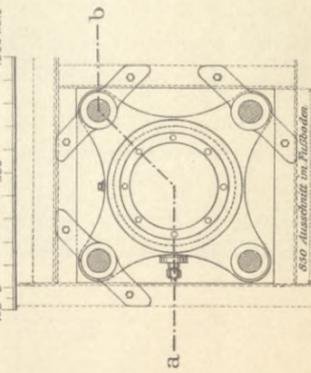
Befestigung auf dem Fußboden der Maschinenkammer.
